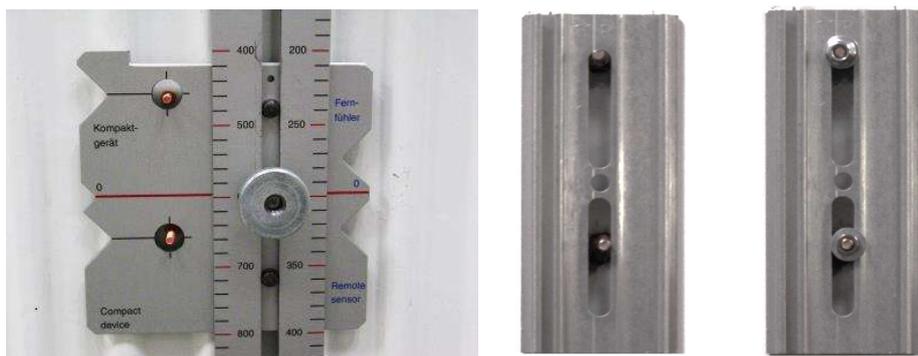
Abstand Schweißbolzen mit Montagelehre und Befestigung des Alu-Wärmeleiters
